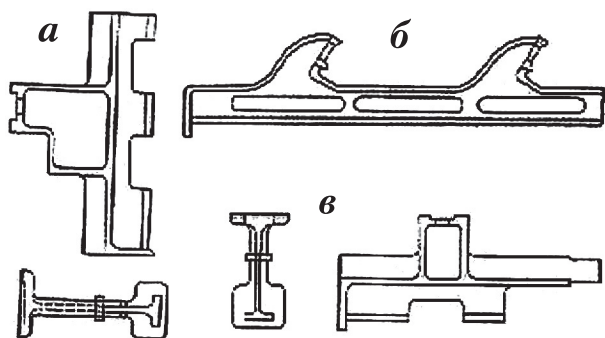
Детали для удержания блоков футеровки стен и подвесных сводов:
